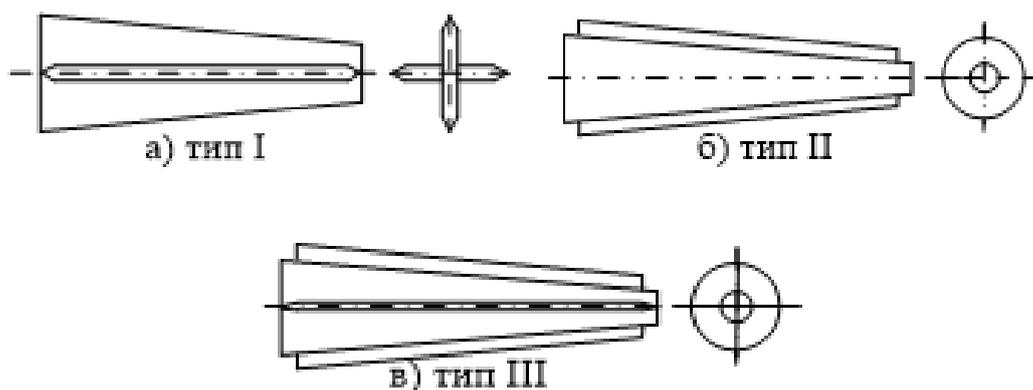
Успокоители потоков: а) крестообразный; б) радиально-трубчатый; в) радиально-трубчатый с пересекающимися пластинами
